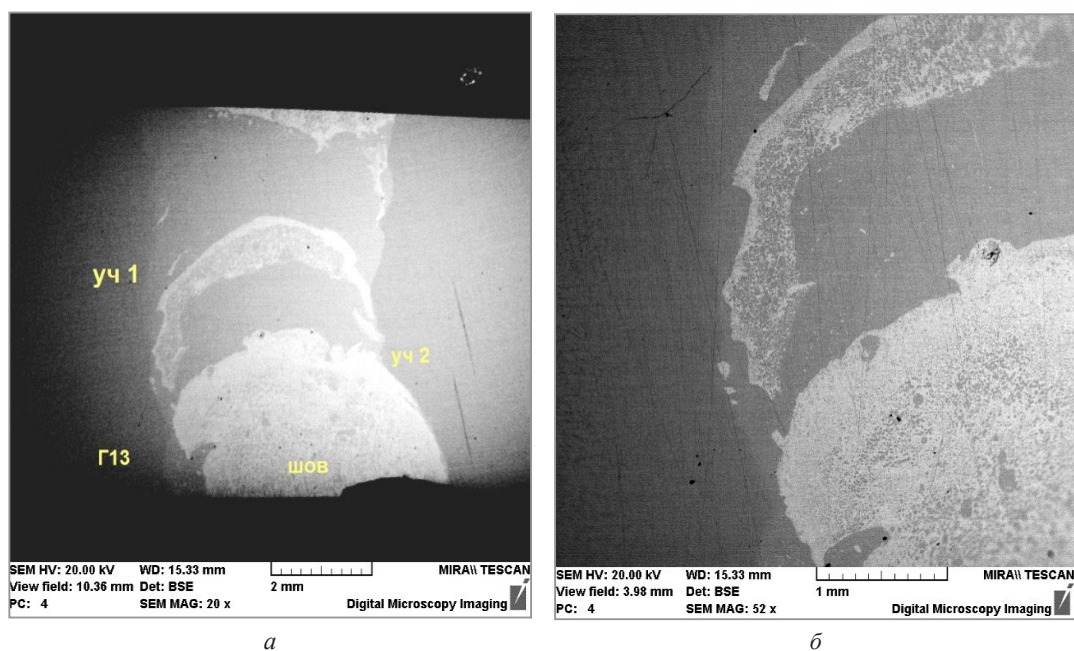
Шов, зона соединения в основной материал из сваренного образца (зона сварки стали 110Г13 и стали Ст. 10 в центральной зоне): *а* – продольный вид; *б* – вертикальный вид
